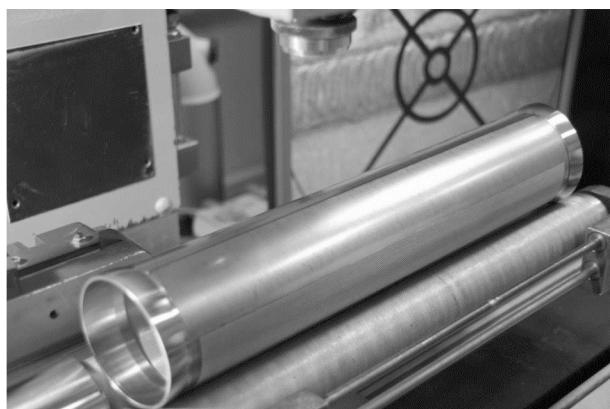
Получение и визуальный контроль продольного и кольцевых сварных швов на фазоразделителе с условным диаметром  $d_{64}$
